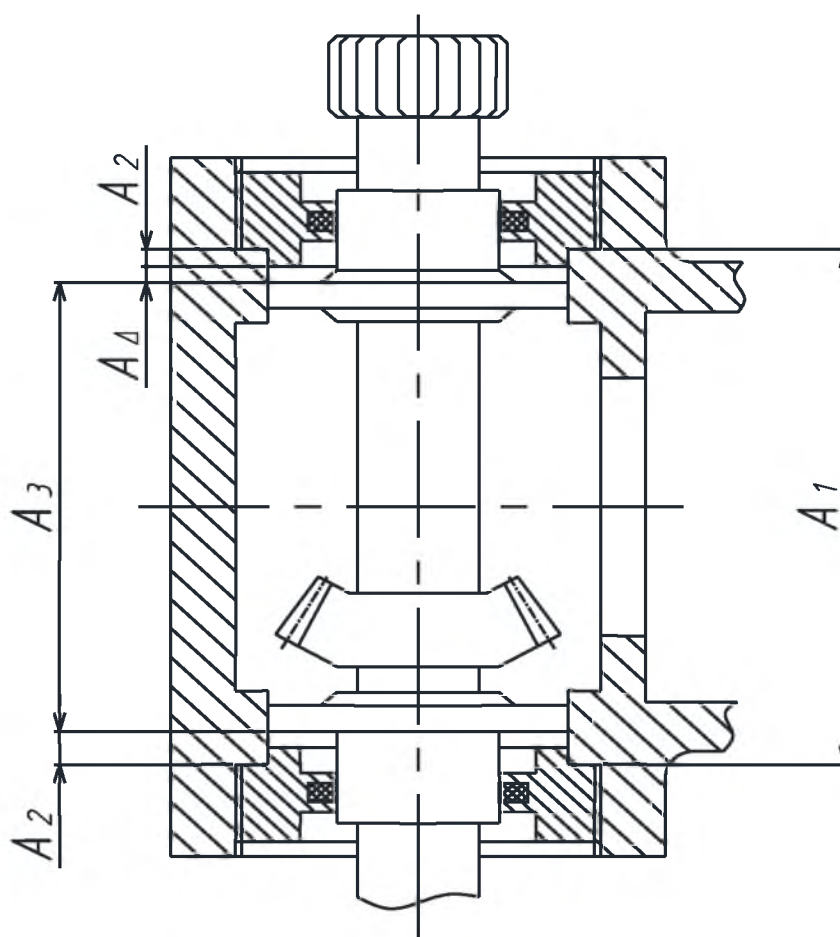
Эскиз узла редуктора винтового подъемника
